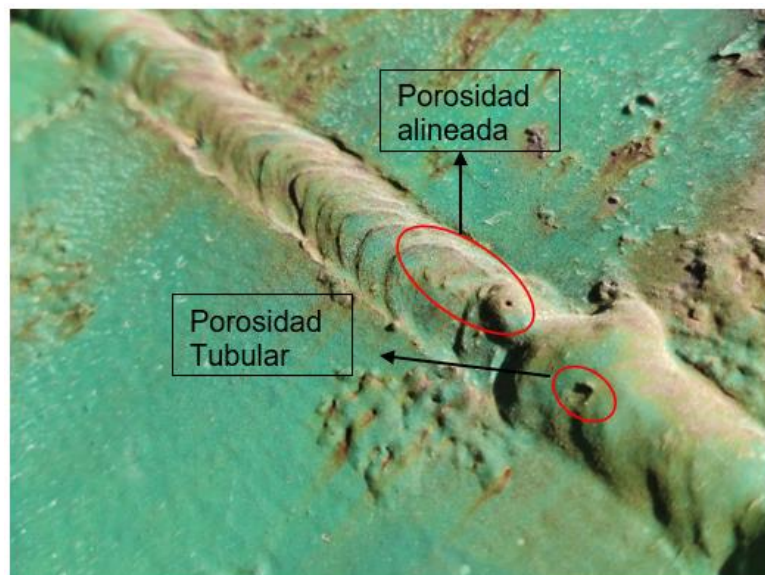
Soldadura con porosidad tubular y alineada
